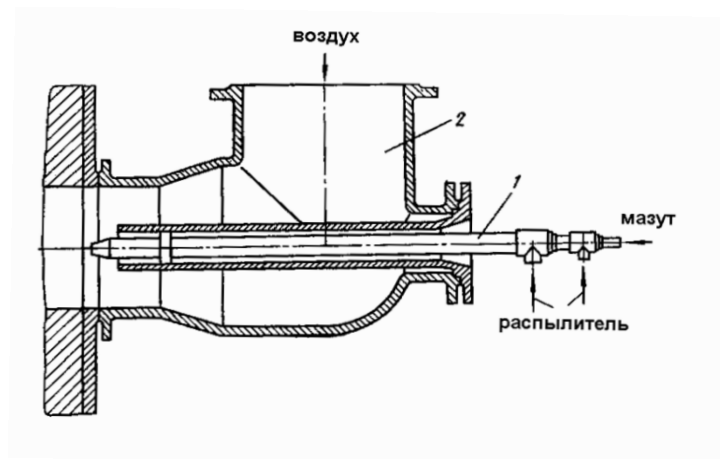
Форсунка высокого давления; 1 – собственно форсунка; 2 – форсуночная коробка
